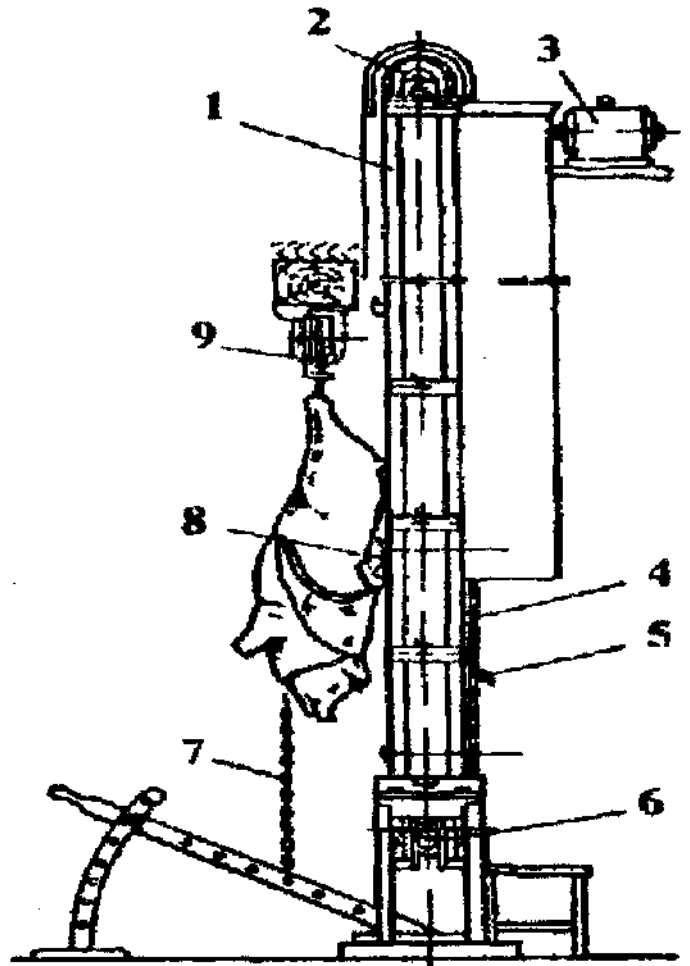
Агрегат вертикального типу для зняття шкур з ту свиней 1 - металевий каркас; 2 - ведуча шестерня; 3 - привід; 4 - тяговий ланцюг; 5 - гак; 6 - натяжна шестерня; 7 - ланцюг гаком; 8 - ланцюг з кільцем; 9 - підвісна дорога.
